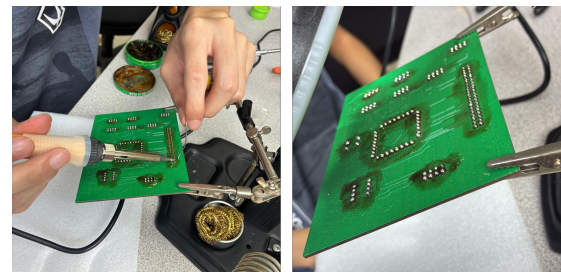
Proceso de soldadura de los componentes pasantes.
